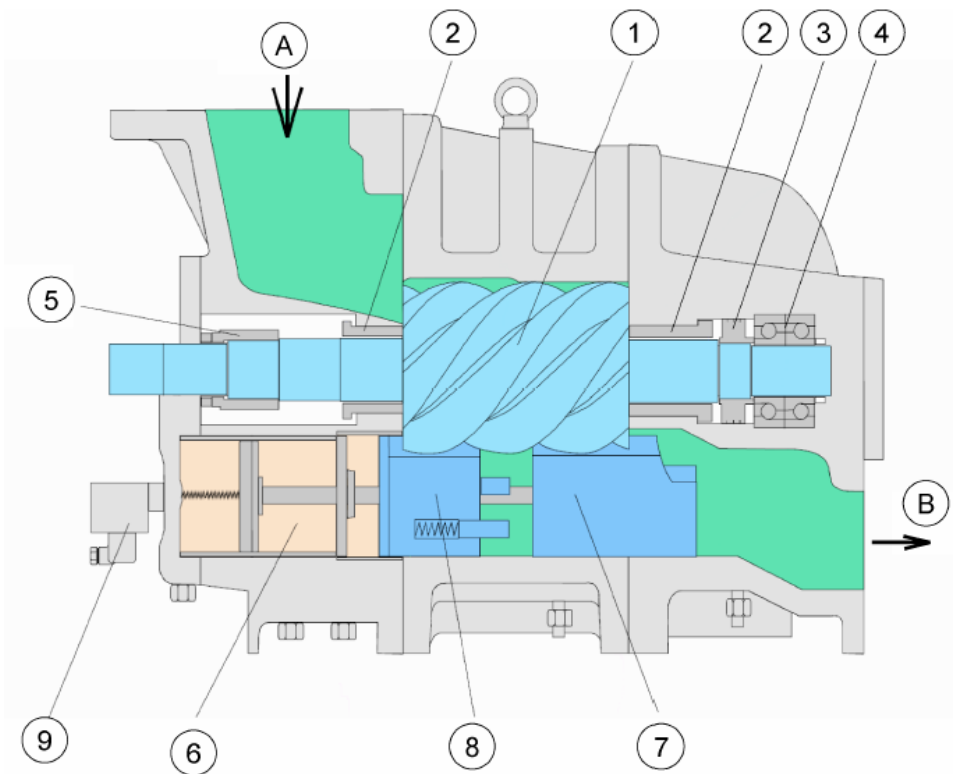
Винтовой компрессор: 1 – главный ротор; 2 – подшипник скольжения; 3 – разгрузочный поршень; 4 – упорный подшипник; 5 – торцевое уплотнение; 6 – гидравлическая система; 7 – регулирующий золотник; 8 – дополнительный золотник; 9 – датчик положения LDS; А – патрубок всасывания; В – патрубок нагнетания
